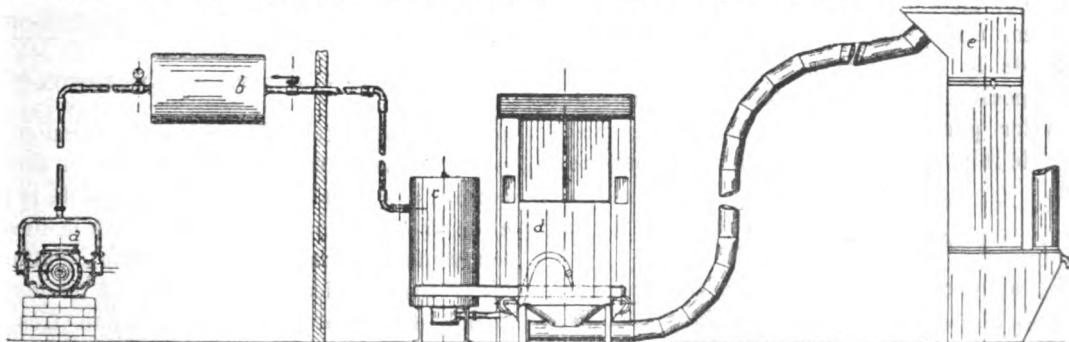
Croquis schématique d'une installation de sablage.
